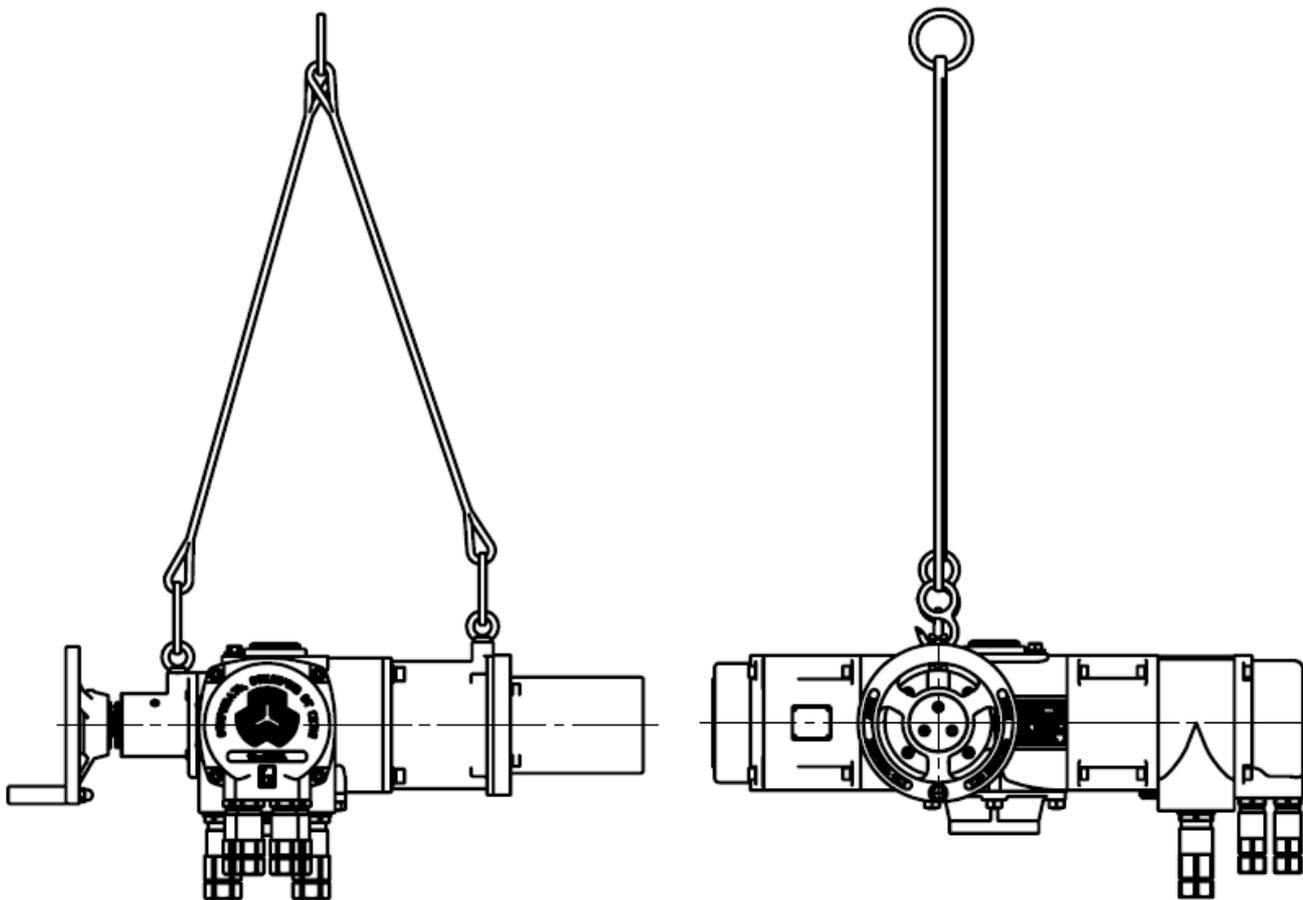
б – Схема строповки привода конструктивной схемы 4
